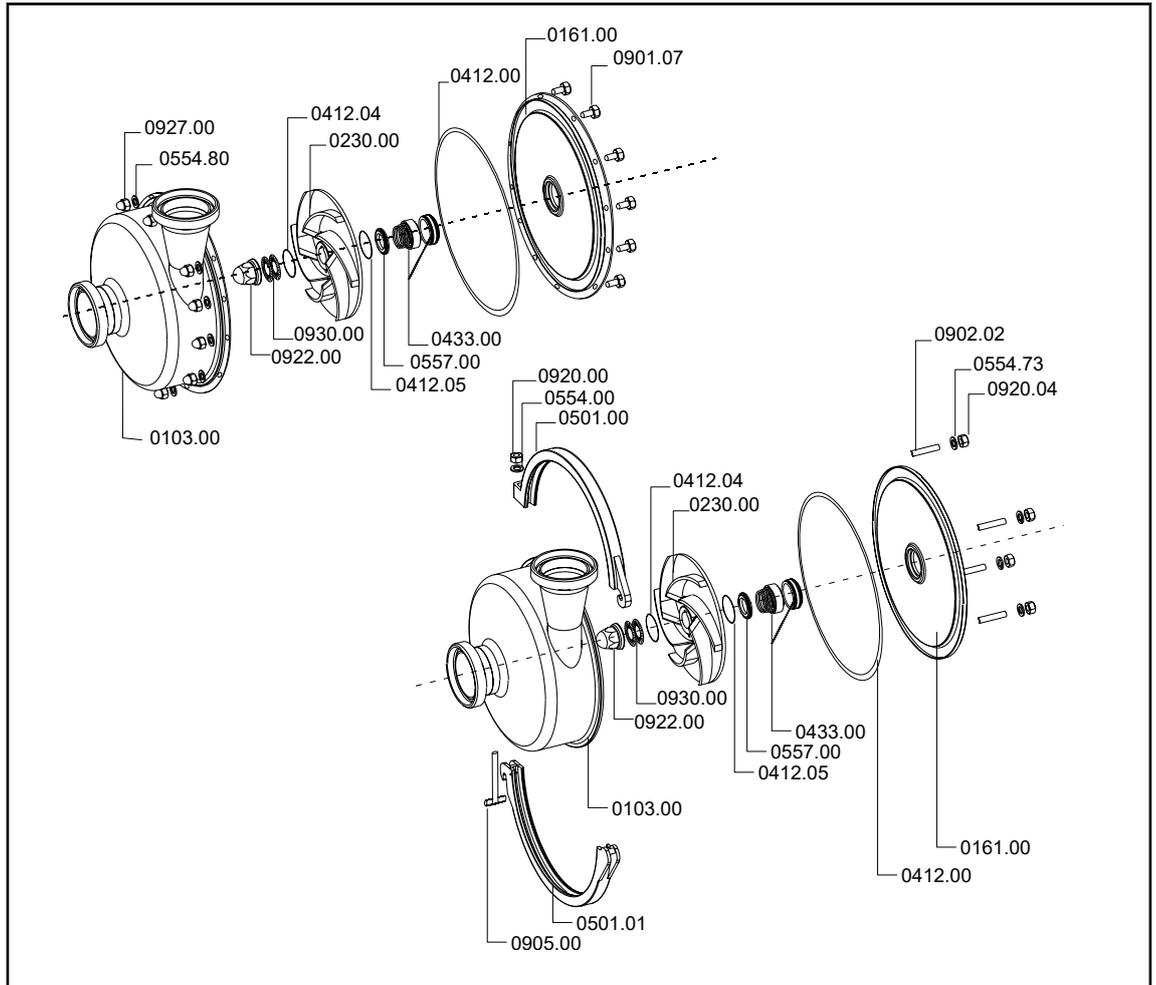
Aperçu des pièces avec différentes variantes de corps : en haut : HPM, en bas KLM
